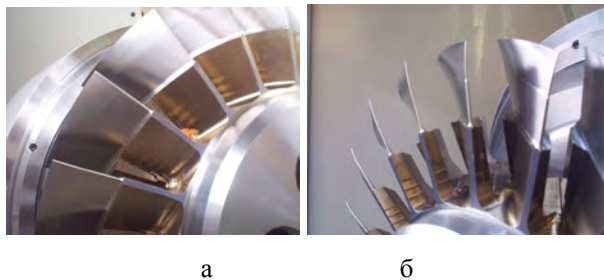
Лопатки осевого колеса компрессора после финишного высокоскоростного фрезерования: а – лопатки со стороны спинки; б – лопатки со стороны выходных кромок
